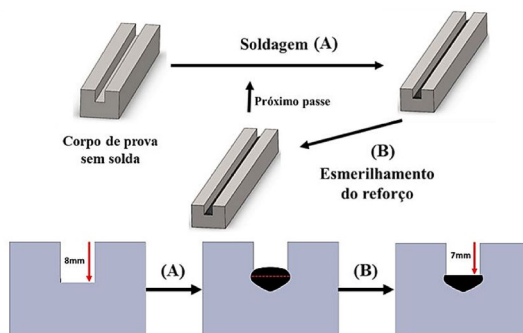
Esquema do corpo de prova esmerilhado com destaque para os processos de soldagem (A) e esmerilhamento (B).
